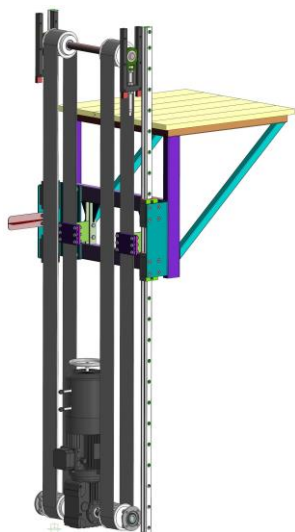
Внешний вид оборудования (привод подъема люка-провала)
